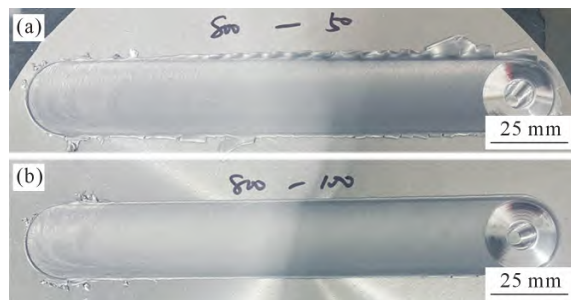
焊缝表面宏观形貌:(a) FSP50; (b) FSP100
